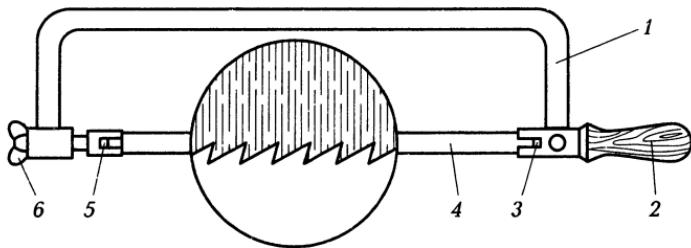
Использование для резки металла цельного ножовочного станка:
